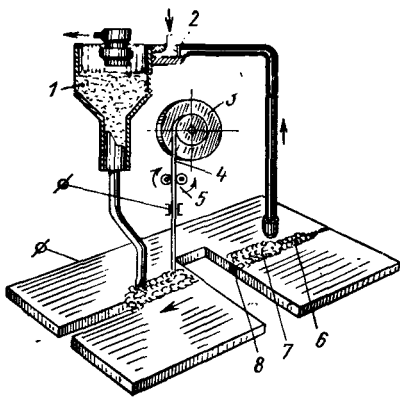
Автоматическая дуговая сварка под флюсом:
